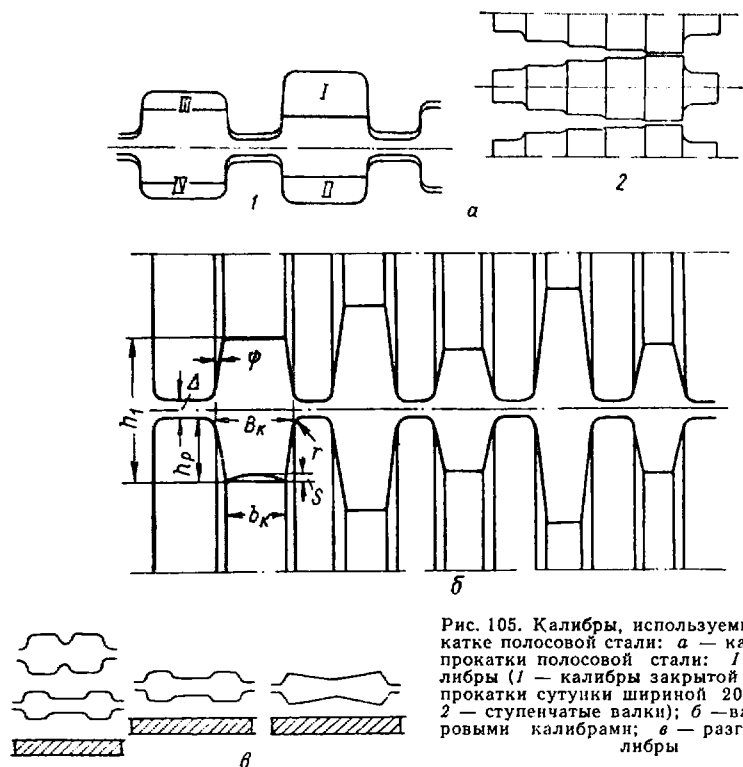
Калибры, используемые при прокатке полосовой стали: а — калибры для прокатки полосовой стали: I—IV — калибры (I — калибры закрытой формы для прокатки сутунки шириной 200—250 мм; 2 — ступенчатые валки); б — валки с ребровыми калибрами; в — разгонные калибры
